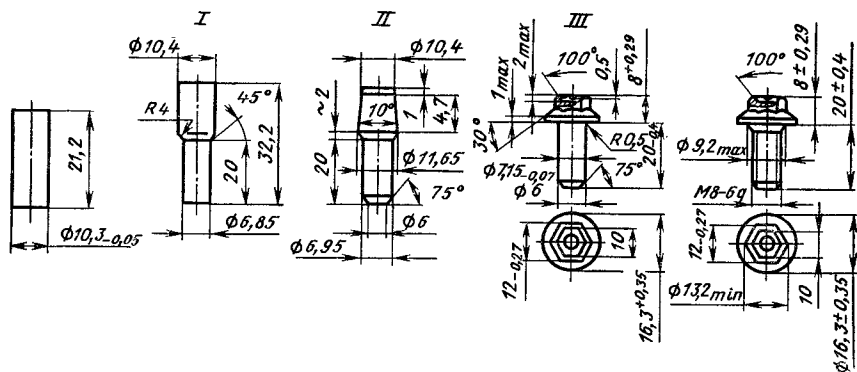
Технологический процесс штамповки и накатки резьбы при изготовлении болтов М8 с фланцем на трехпозиционном холодновысадочном и резьбонакатном автоматах 13ВОА-8Ф и АР-12Ф
